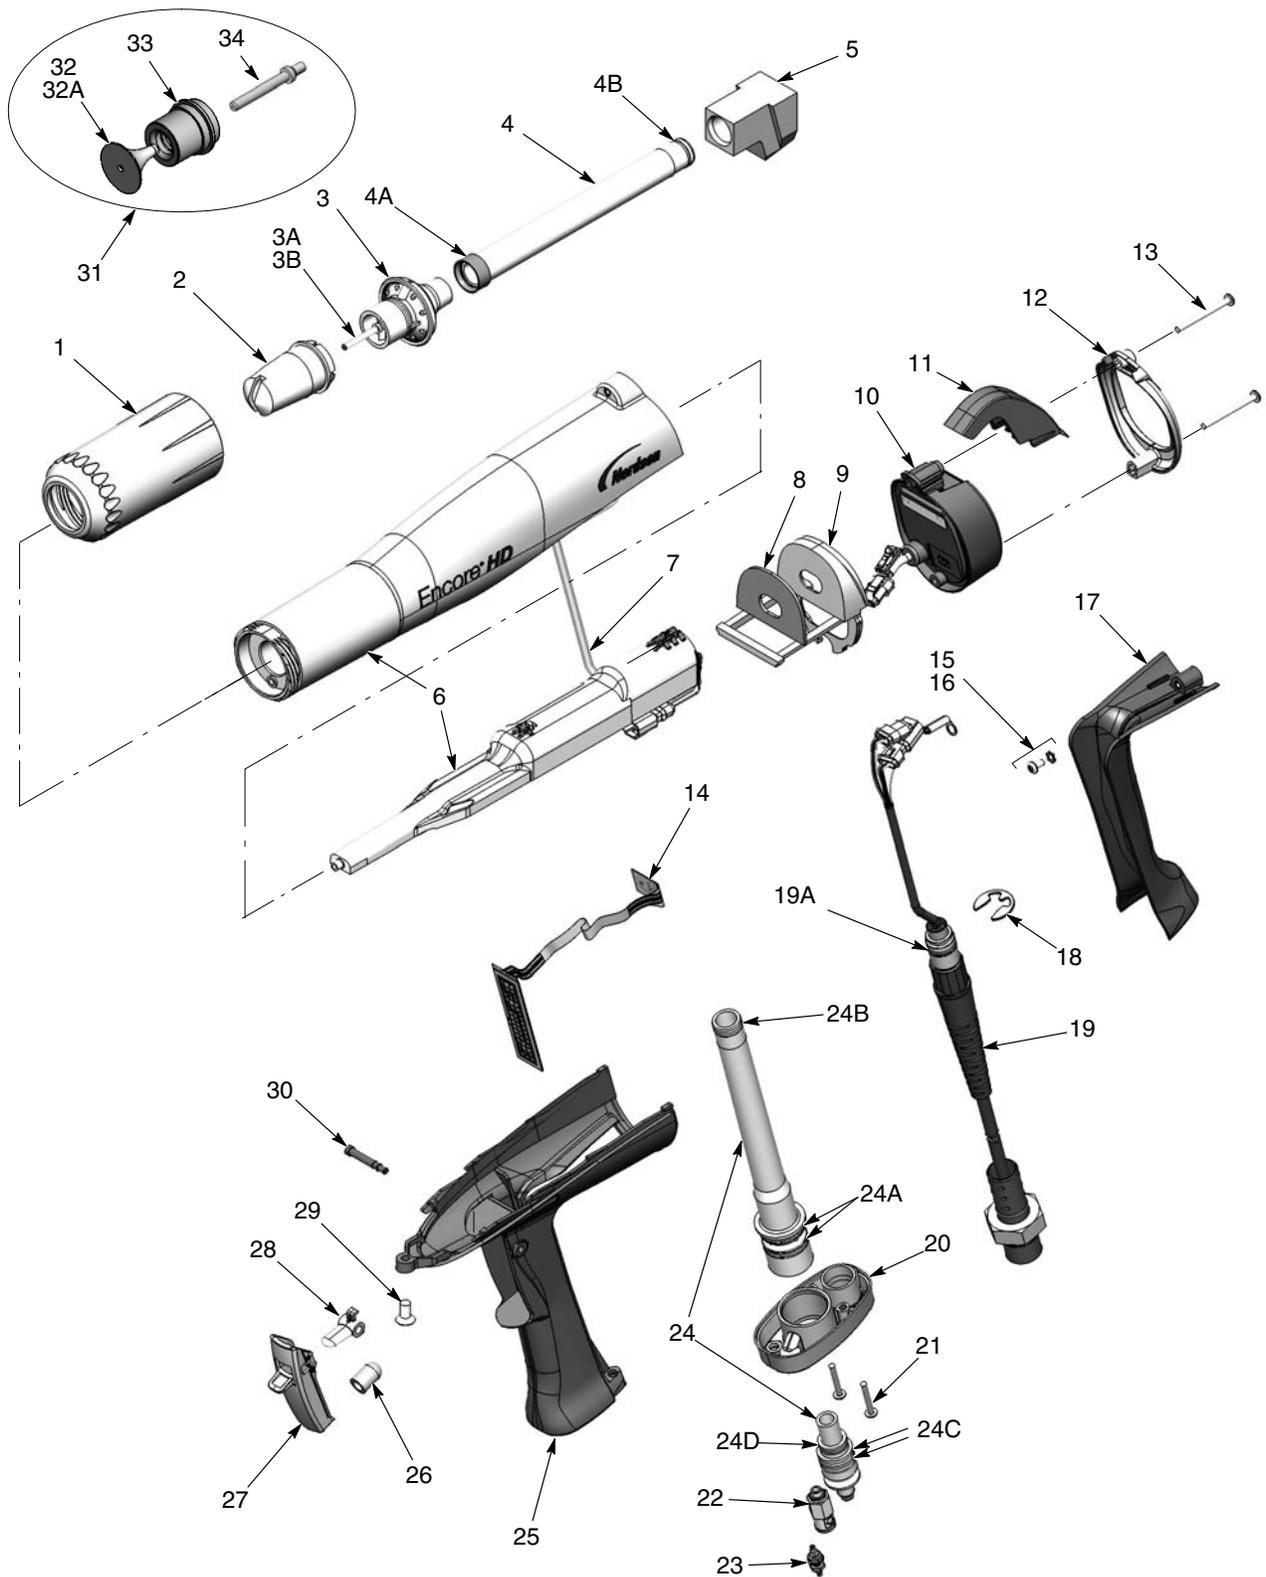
Vista explodida da pistola manual para pintura Encore HD e acessórios
